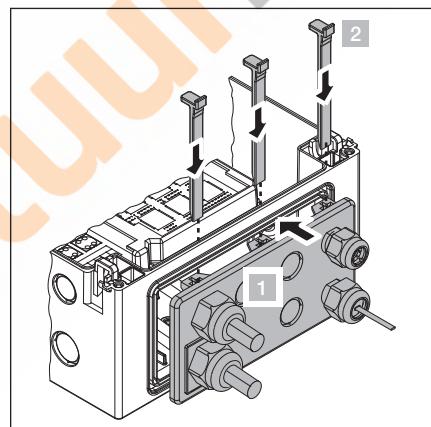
Einbau der Verschraubungsflanschplatte
